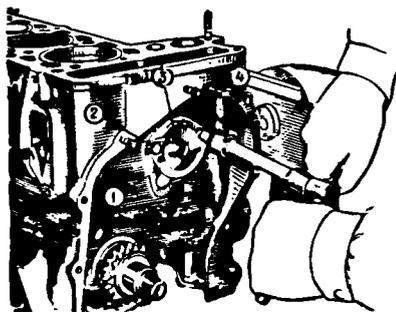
Снятие валика привода масляного насоса: 1 - упорный фланец; 2 - болт крепления фланца; 3 - валик привода масляного насоса; 4 - ключ
